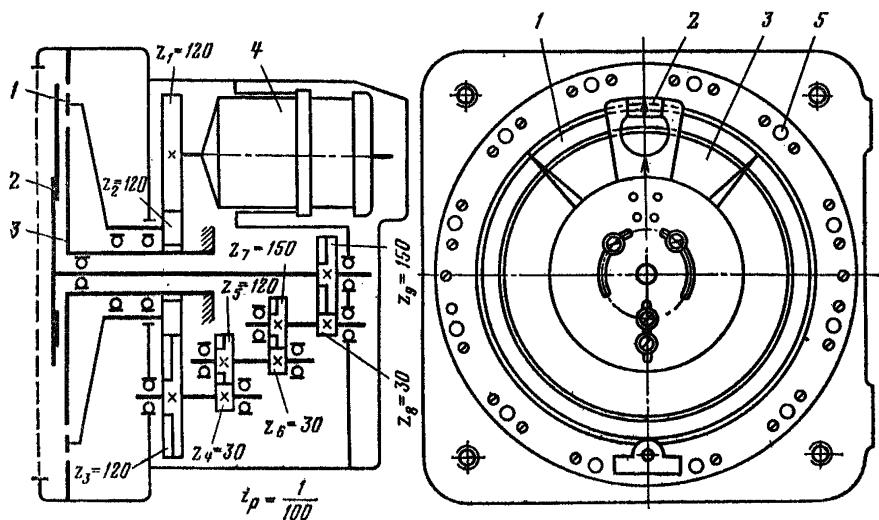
Кинематическая схема указателя глубины УГС-4; 1 — кольцевая шкала точного отсчета; 2 — визир грубого отсчета; 3 — неподвижная шкала; 4 — сельсин; 5 — лампа подсветки шкалы
